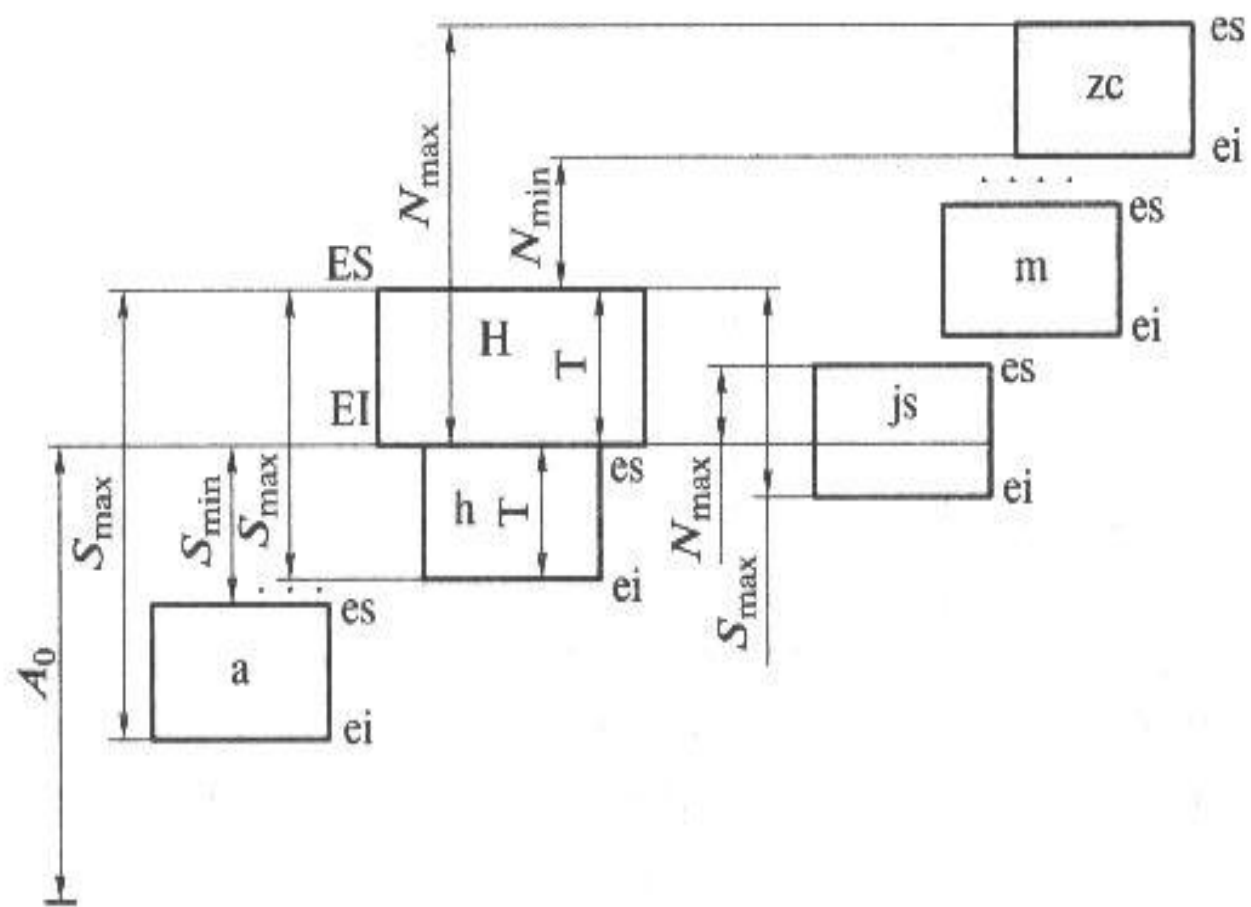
Схема расположения полей допусков в системе отверстия
